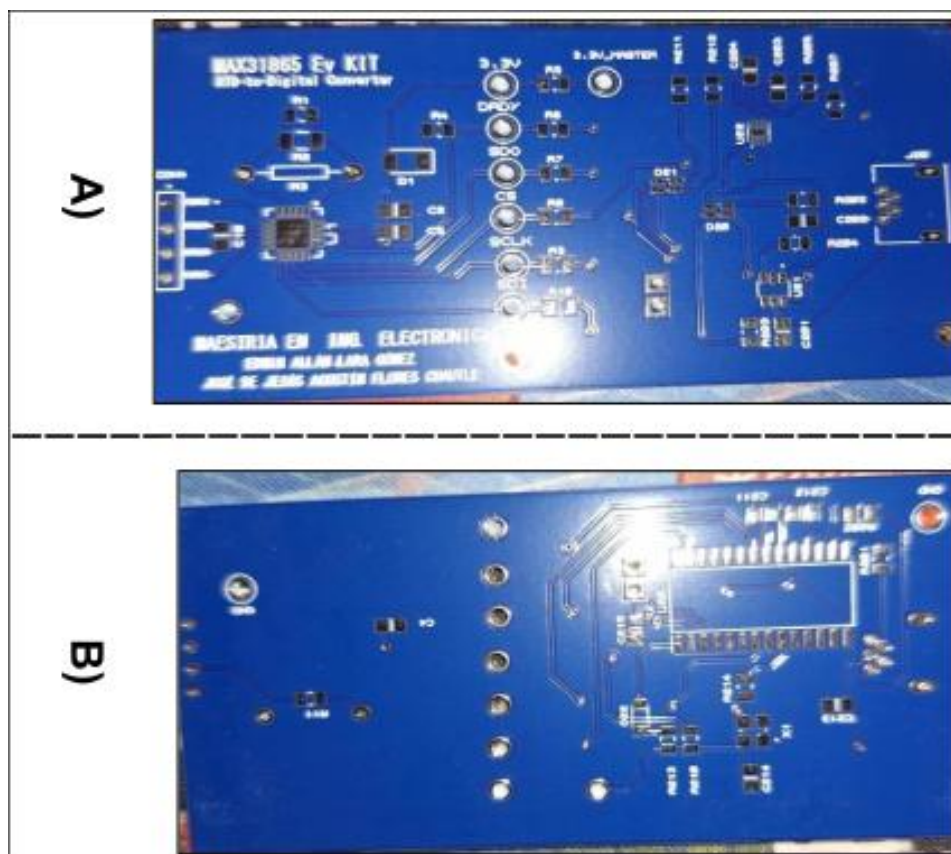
A) Vista superior y B) vista inferior de la PCB sin componentes del MAX31865EVKIT.
